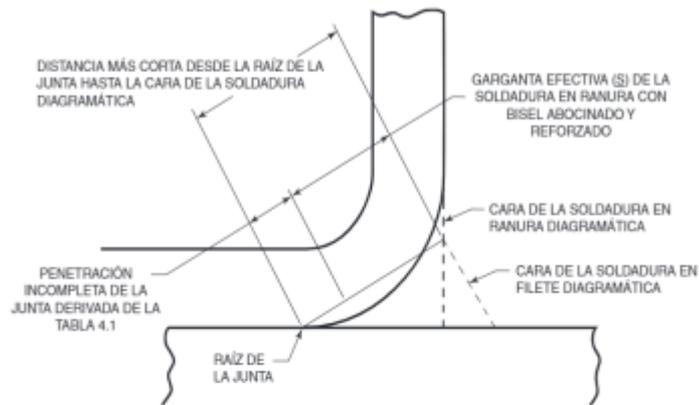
Soldadura en ranura de bisel abocinado con soldadura en filete reforzada (ver 4.4.2.7)
